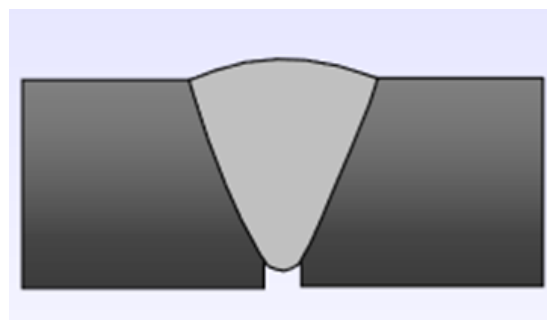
Penetrarea incompletă a rădăcinilor. Sursă: M.S. Rogers, Welding Inspection Defects/Repairs Course Reference WIS 5, 2003.
